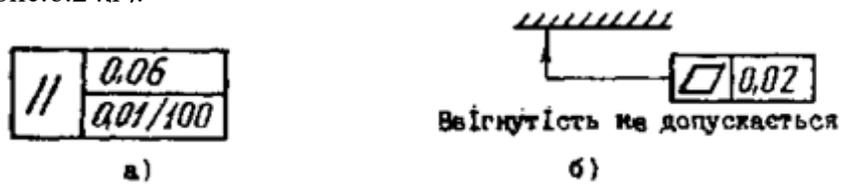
Схеми позначення допусків форми і розміщення
